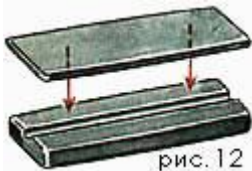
Изготовление корпуса девона из двух пластин разной толщины
